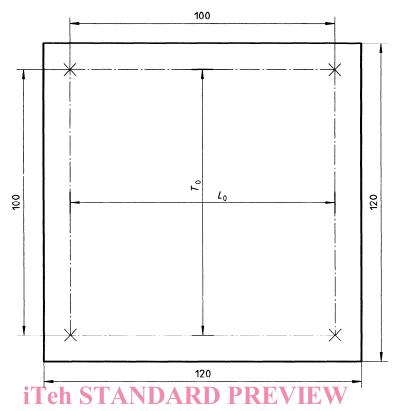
Dimensions des éprouvettes et longueurs entre repères
